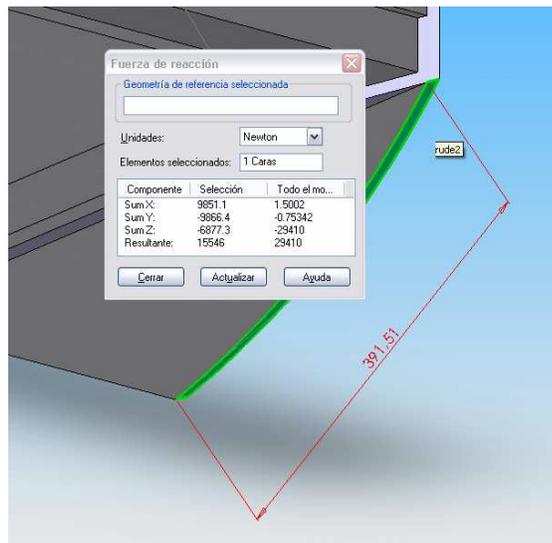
Fuerzas de Reacción en la Soldadura Bafles
